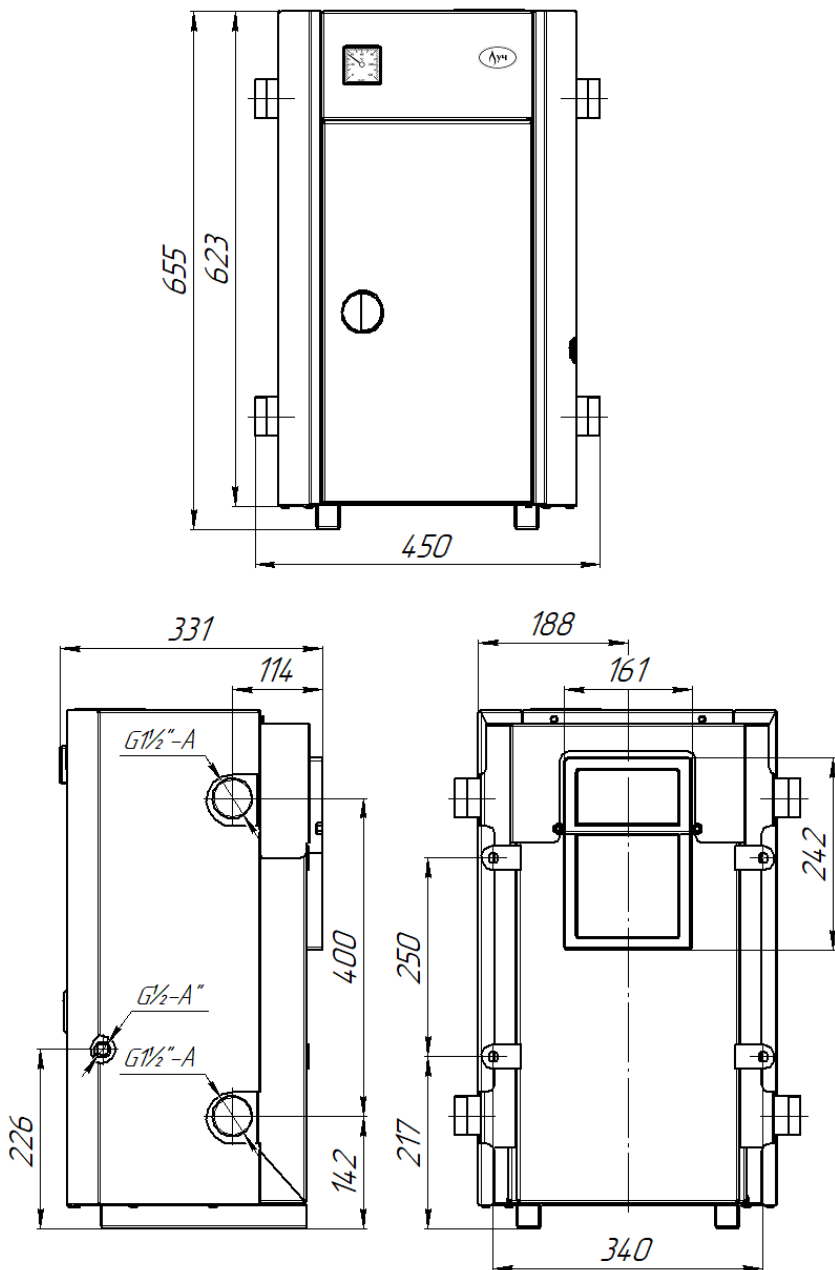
Габаритные и присоединительные размеры КСГ – 8П
